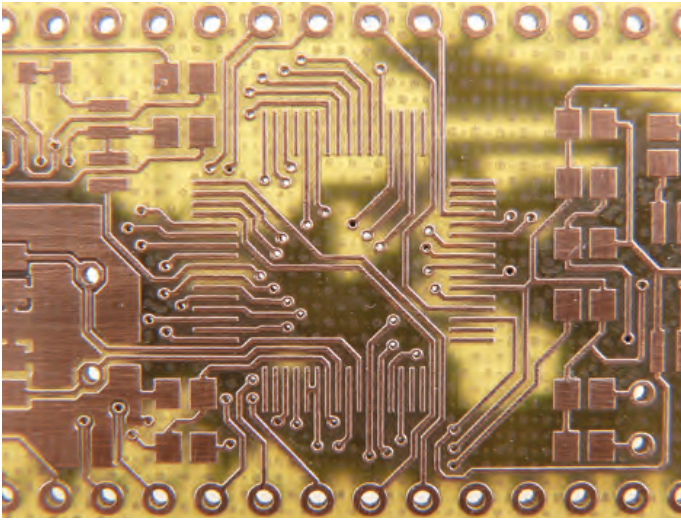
Detailsansicht einer vom Elektor PCB Prototyper gefrästen Platine. Die Breite einiger gefräster Bahnen beträgt nur 0,15 mm.
